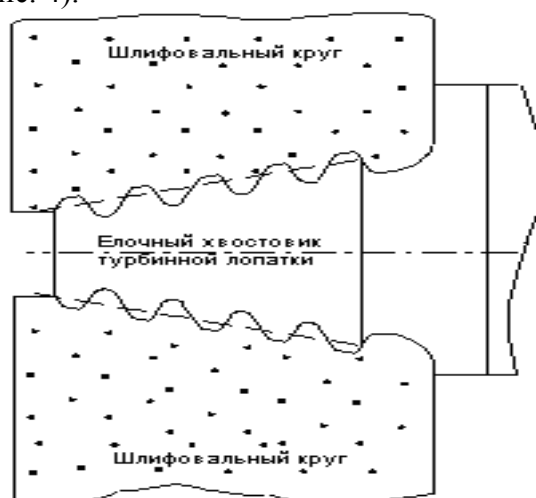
Схема шлифования "ёлочного" хвостовика лопатки ГТД
